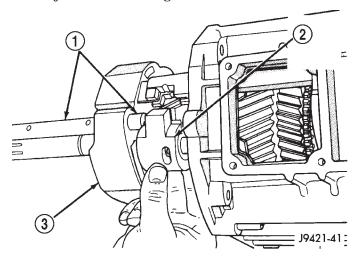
CONJUNTO DE PALANCA Y CASQUILLO
